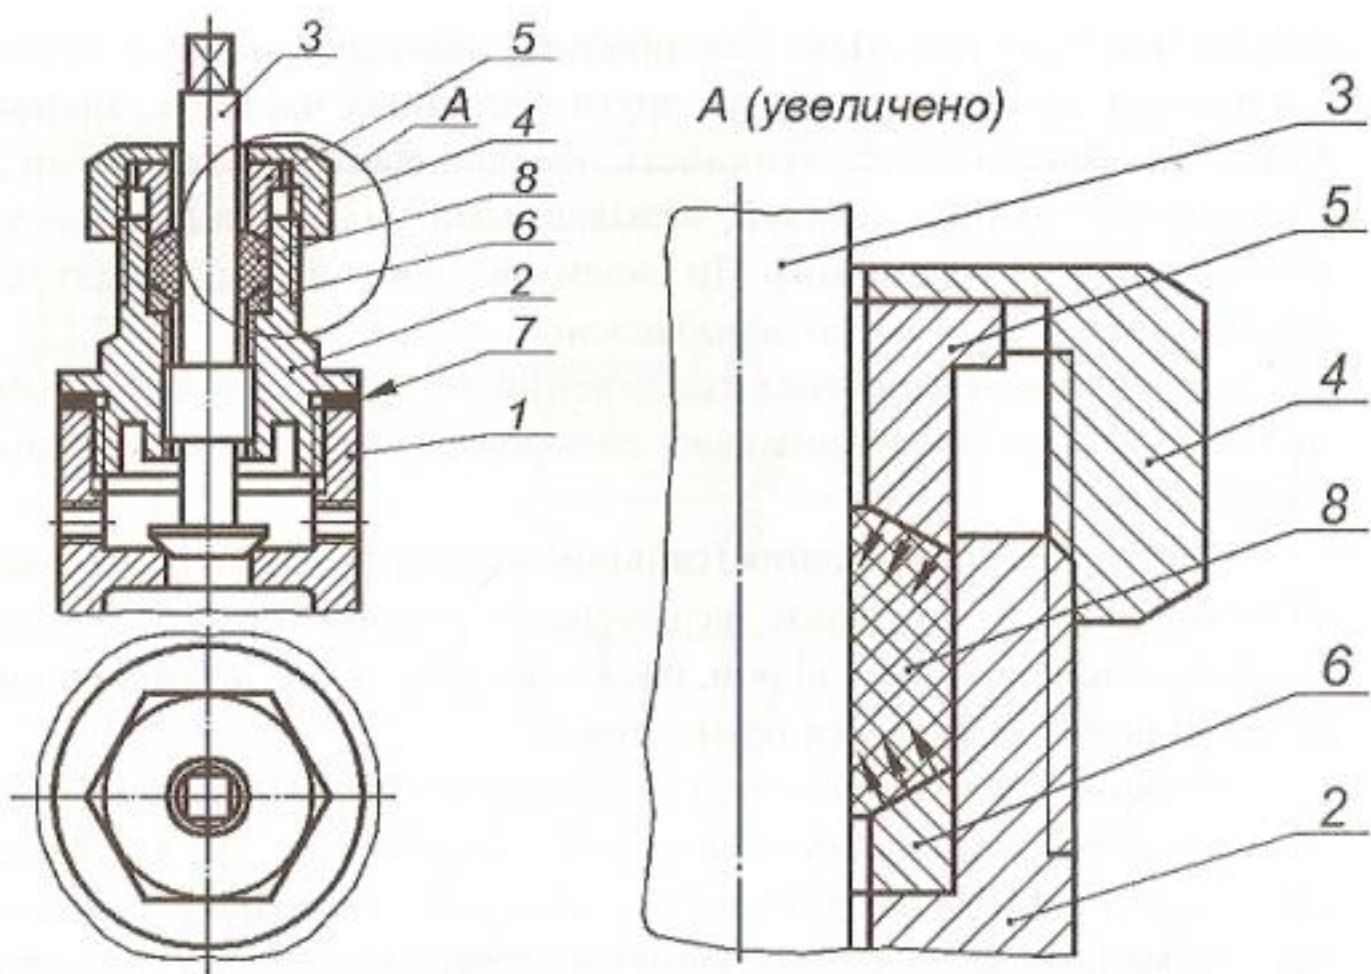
Сальниковое уплотнение шпindelной резьбовой пары (фрагмент вентиля: 1 – корпус; 2 – крышка; 3 – шпindel; 4 – гайка-накидная; 5 – втулка нажимная; 6 – кольцо опорное; 7 – прокладка; 8 – уплотнитель)
